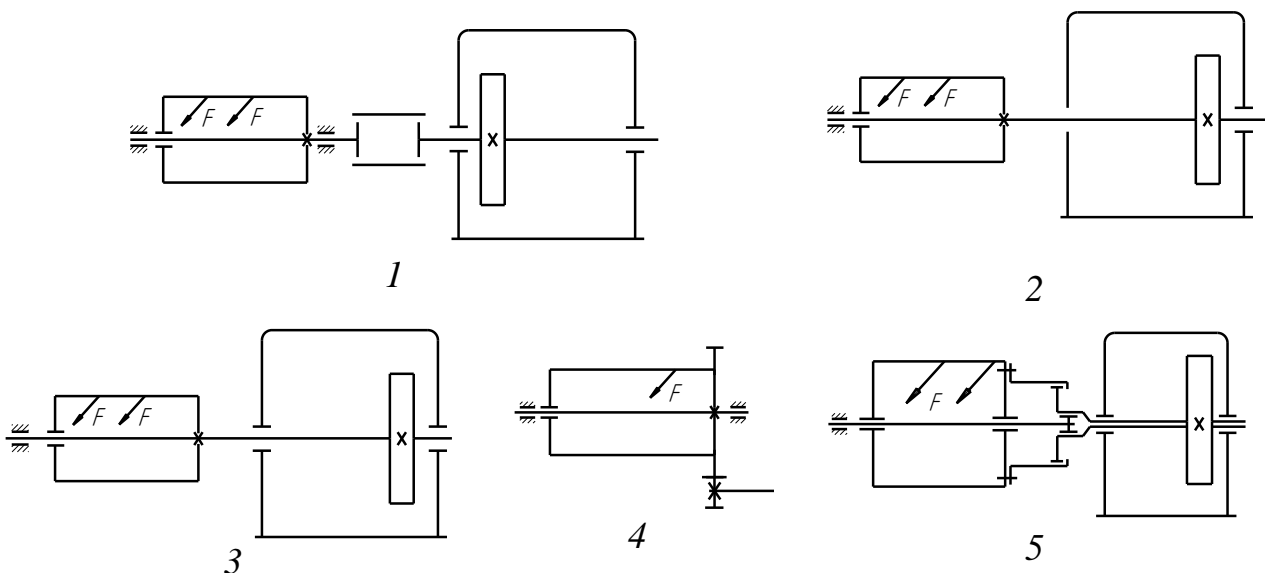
Схемы соединения барабана с редуктором
